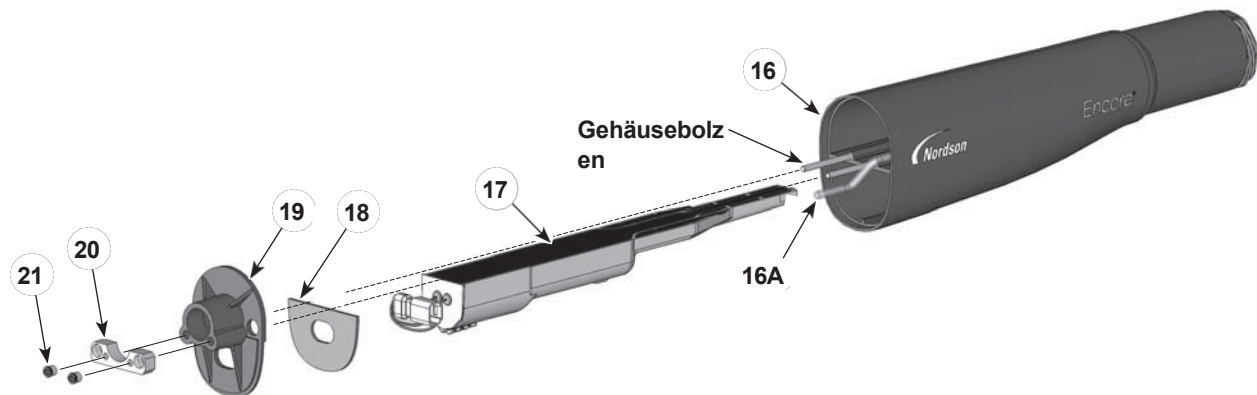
Demontage der Pistole - Austausch des Netzteils
